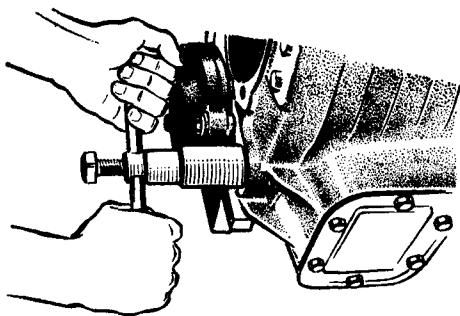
Выпрессовка оси блока шестерен заднего хода
